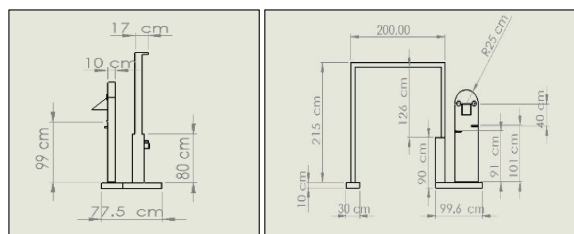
Planos Pieza 1: estructura o Armazón. Fuente: Elaboración propia
